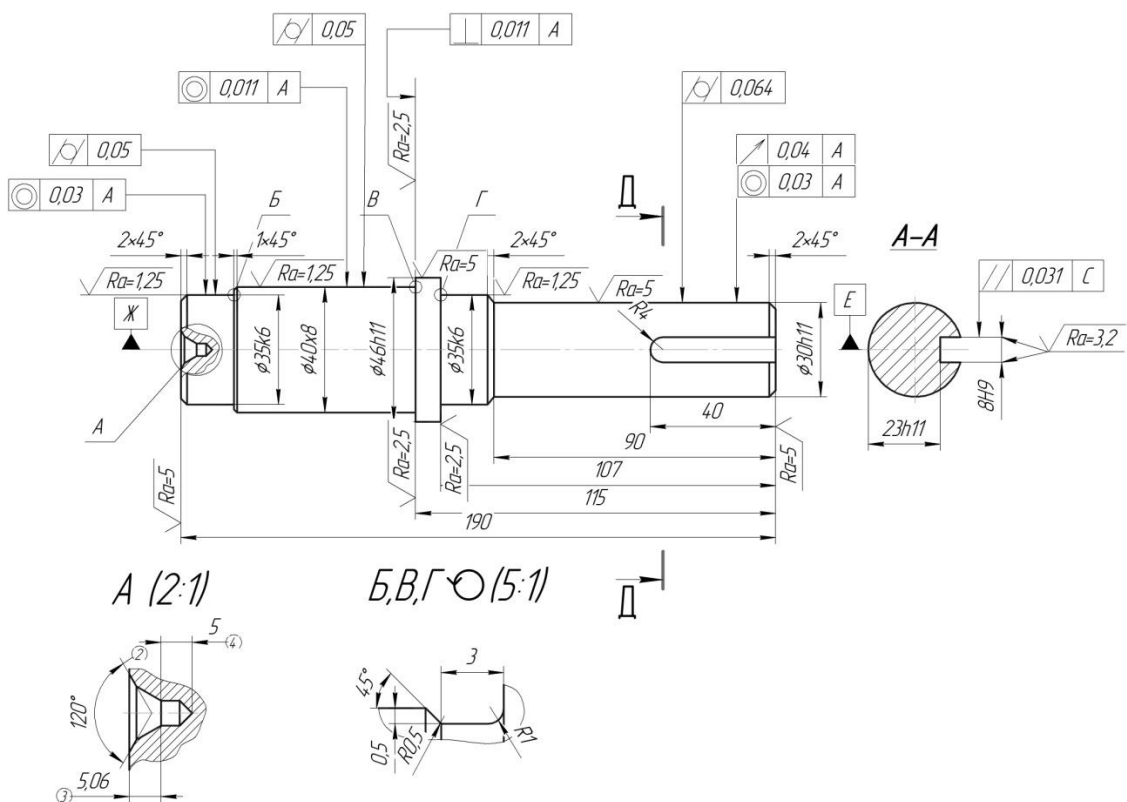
Робоче креслення типової деталі представника «вал тихохідний»
